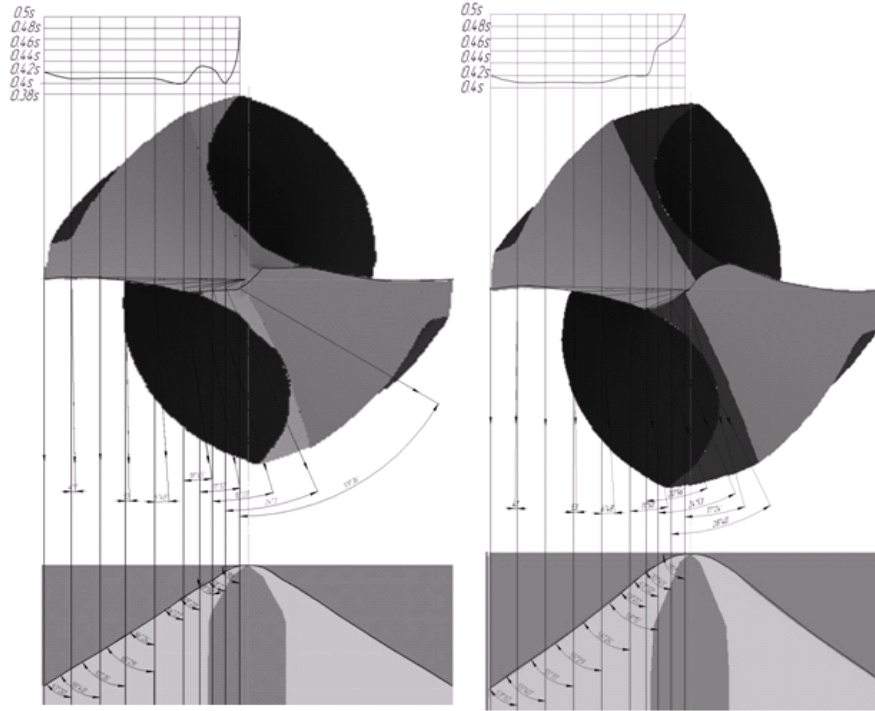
Толщина среза при сверлении сверлом с подточкой формы С и с круговой подточкой поперечной режущей кромки
